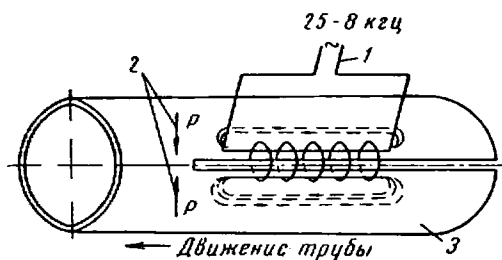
Принципиальная схема индукционной сварки труб
